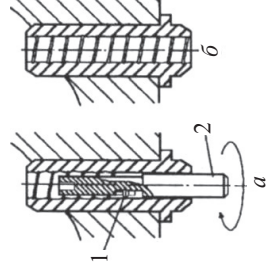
Ремонт отверстия направляющей втулки клапана с помощью специального приспособления – раскатки (роллера): а – нарезание внутренней резьбы; б – отверстие после обработки разверткой в размер стержня клапана; 1 – ролик из твердого сплава; 2 – роллер
